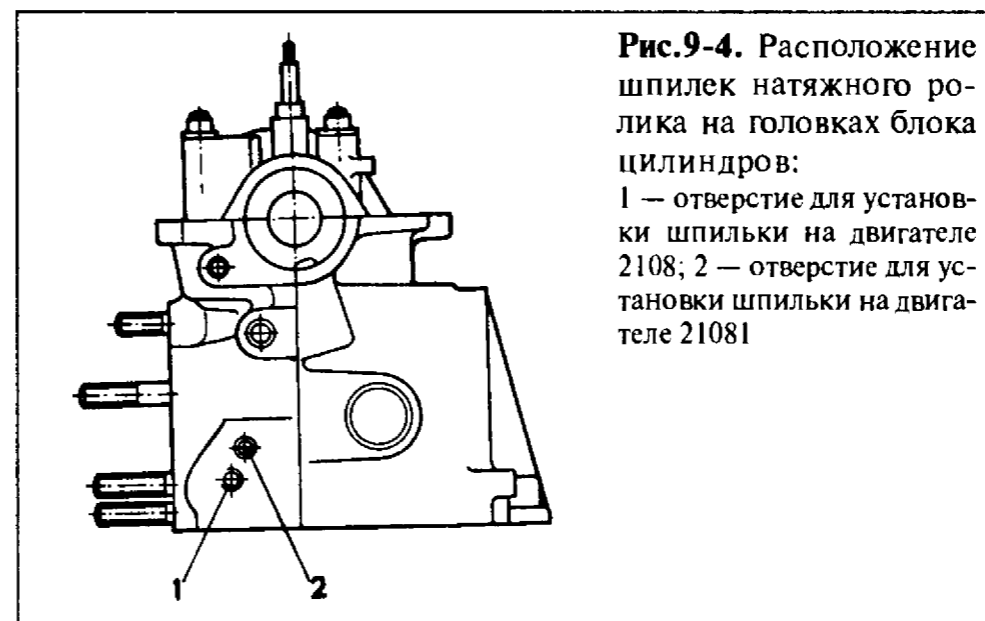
Расположение шпилек натяжного ролика на головках блока цилиндров: 1 — отверстие для установки шпильки на двигателе 2108; 2 — отверстие для установки шпильки на двигателе 21081
